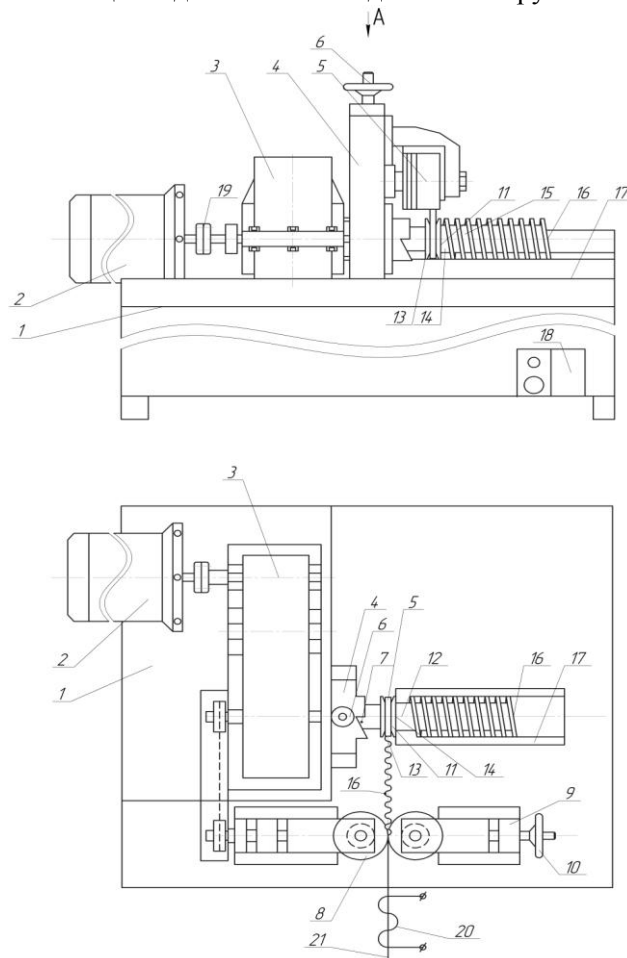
Пристрій для виготовлення гвинтових гофрованих заготовок з різним профілем гофр
